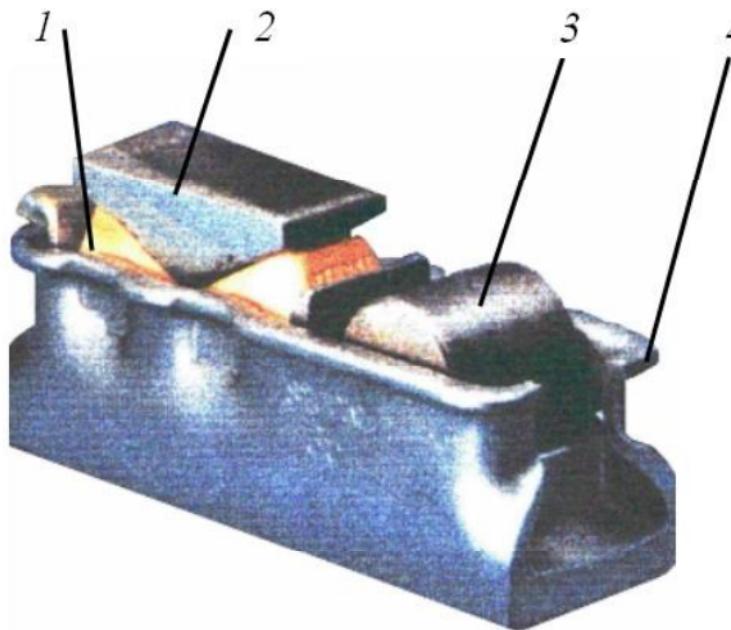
Пружно-катковий ковзун, розроблений фірмою «А. Стакі»
